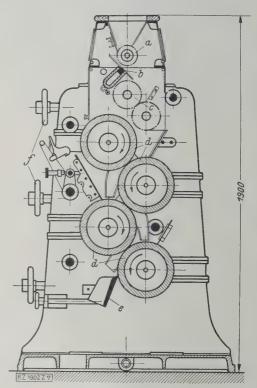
Kakaowalzenmühle, Bauart Bauermeister.
